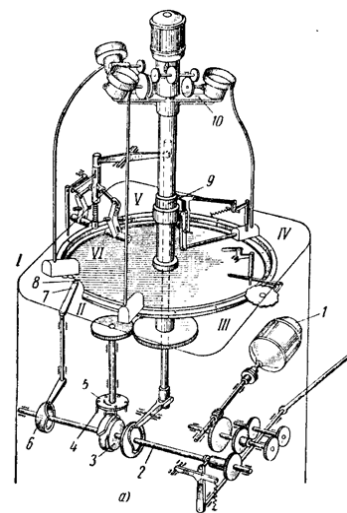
Схема полуавтомата для сборки ушка ручных часов
